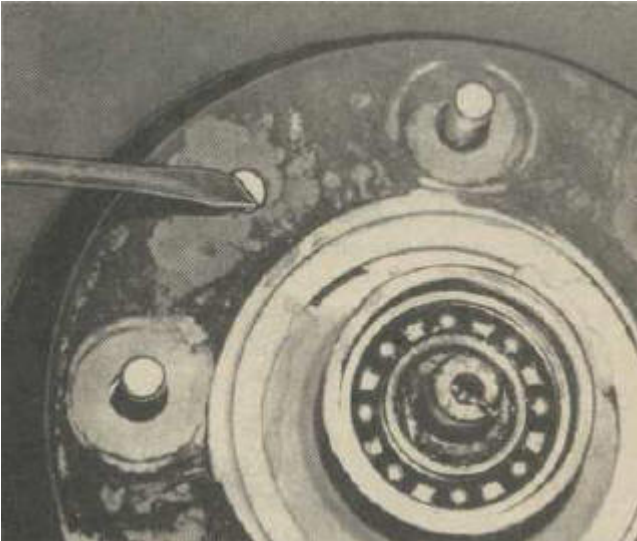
Sicherungsschraube der Bremstrommel mit einem Schraubendreher lösen
